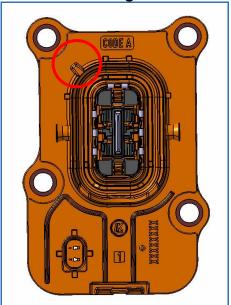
Steckerleiste KHV 600, 1-polig, Kodierung A zum Steckhülsengehäuse
